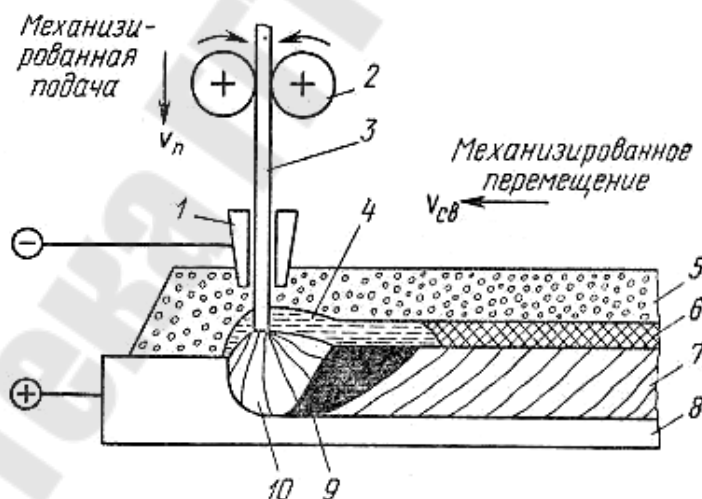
Схема автоматической дуговой сварки под флюсом
